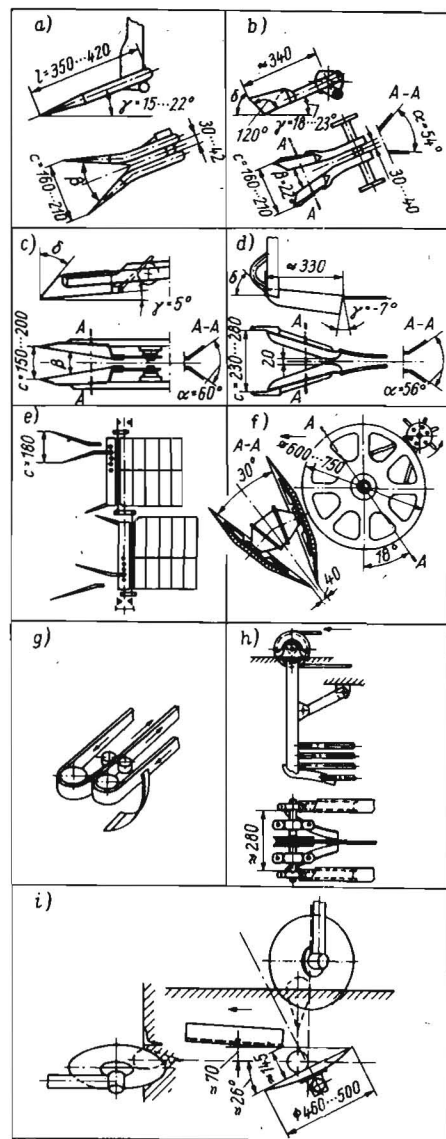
Typen von Rodewerkzeugen; Erläuterung im Text
